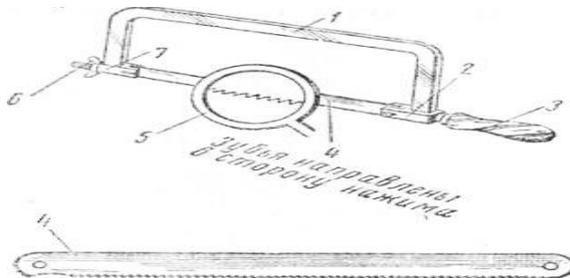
Ножовка: 1 — станок, 2 — неподвижная серьга, 3 — рукоятка, 4 — ножовочное полотно, 5 — лупа, 6 — барашек, 7 — подвижная серьга
